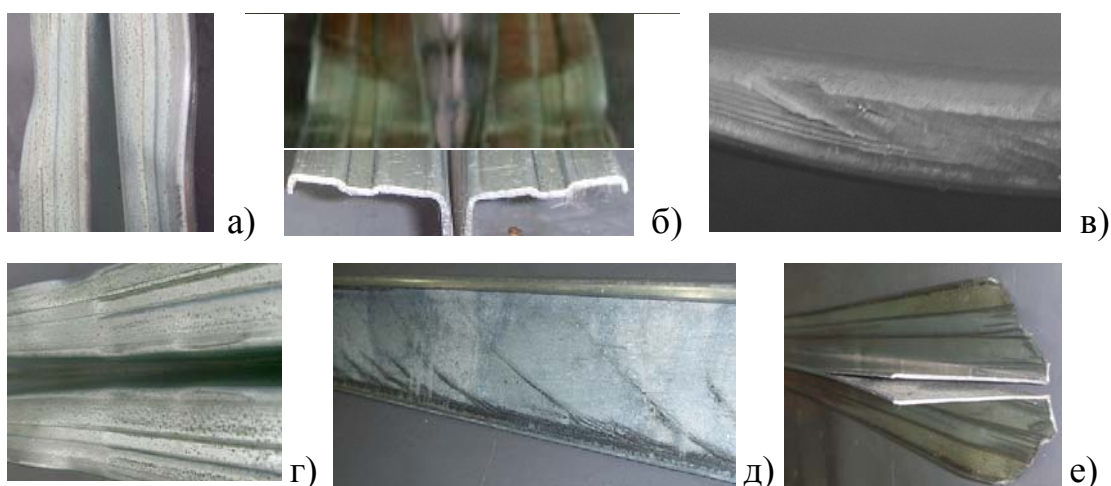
Дефекты заготовки Т-образного профиля при её формовке:
